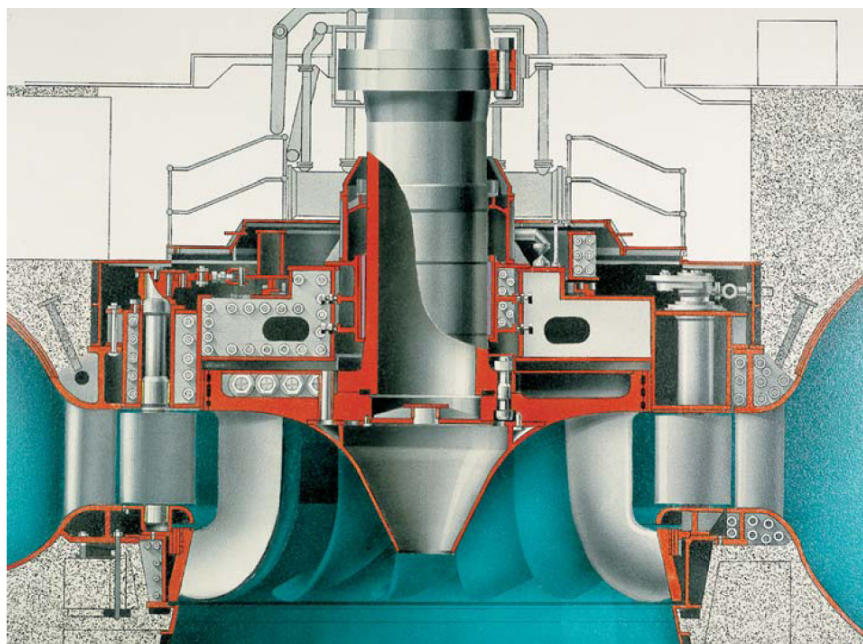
Turbina Francis (OJSC Power Machines, 2004).
